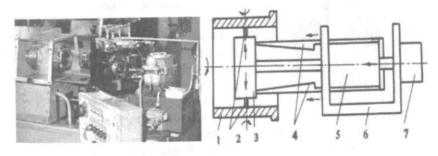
Внешний вид и принципиальная схема полуавтомата для фрикционного латунирования цилиндров двигателя вращающимся штифтом:
